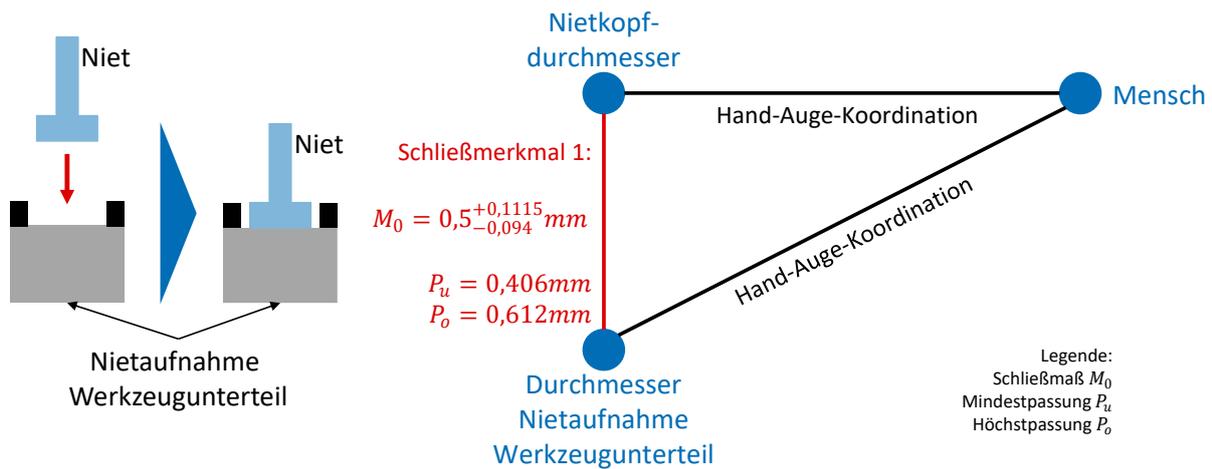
Prozess für das Fügen des Nieten auf dem Werkzeugunterteil und die Toleranzkette (TK1)
